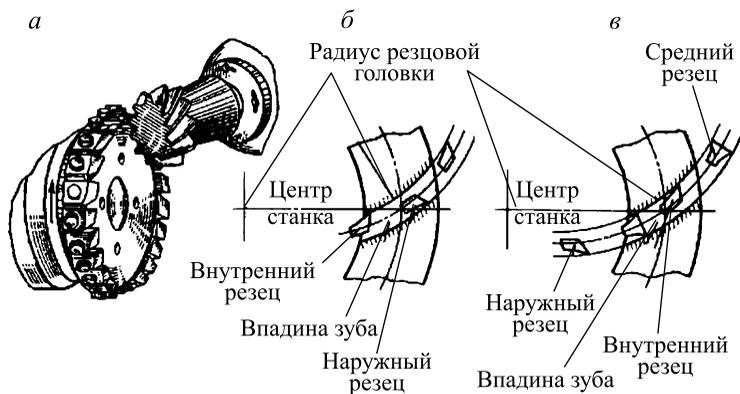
Схемы нарезания конического зубчатого колеса с криволинейными зубьями
